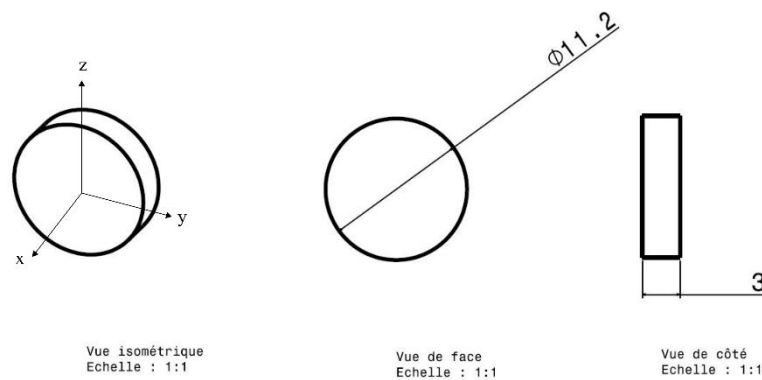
Dimensions de l'éprouvette cylindrique.
